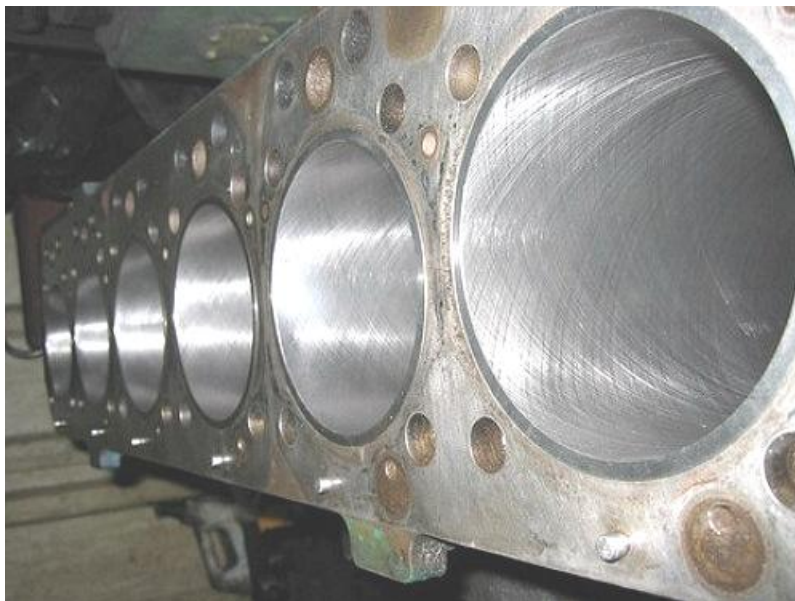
Блок двигателя с нанесенным хоном на стенки цилиндра
